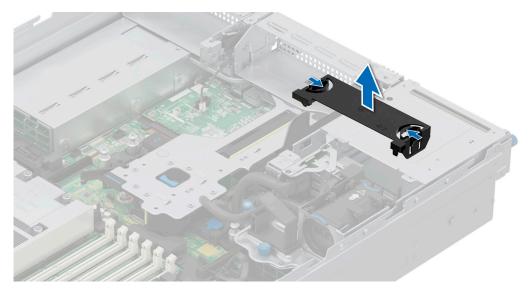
Entfernen des Kühlgehäuses für das hintere EDSFF E3.S-Laufwerksmodul
